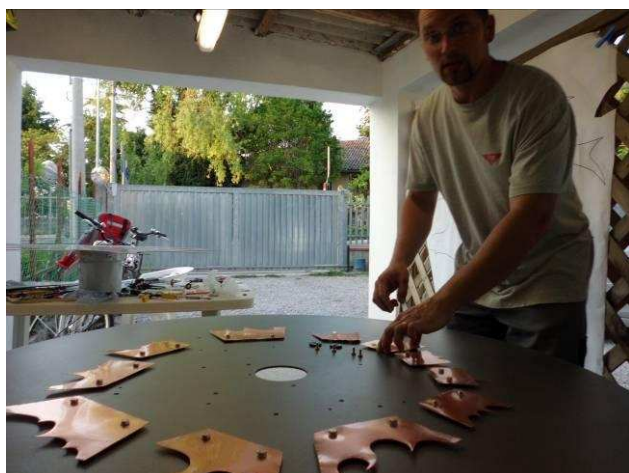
I piccoli raggi in rame del sole sono fissati sul piano tondo d'acciaio.
